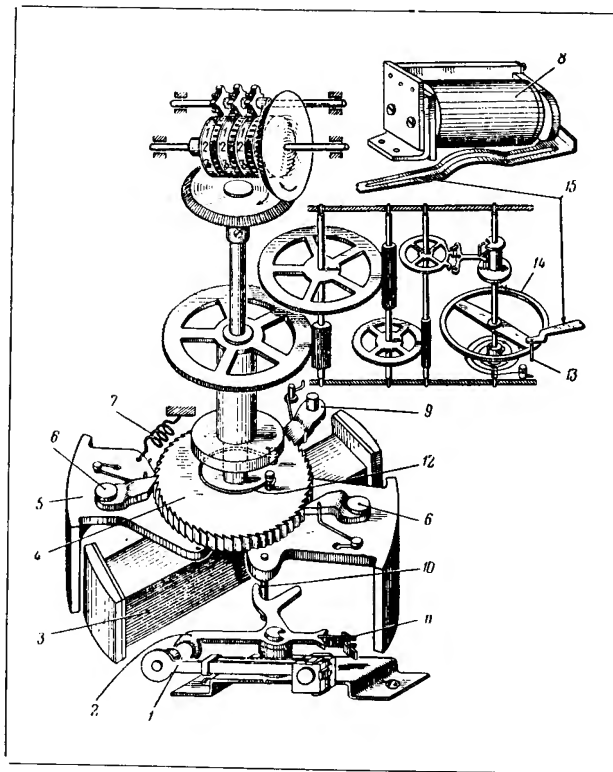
Принципиальная схема счетчика: 1 — контакт; 2 — рычаг с контактом; 3 — электромагнит подзавода; 4 — храповое колесо; 5 — якорь; 6 — собачки; 7 — пружина; 8 — электромагнит; 9 — собачка; 10 — штифт; 11 — пружина; 12 — вспомогательная пружина; 13 — штифт; 14 — баланс; 15 — рычаг.
